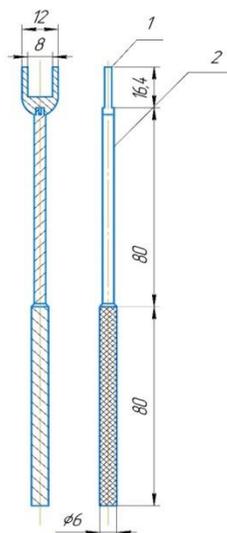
Оснастка для установки эндопротеза межпозвоночного диска патент RU 2538891: 1 – вилка; 2 – рукоятка
